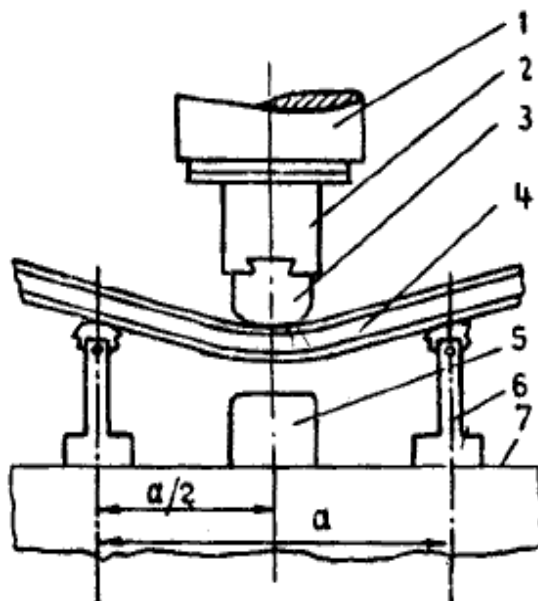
Схема правки (гибки) на прессах типа ПП-250: 1 – плунжер пресса; 2 – поворотный адаптер; 3 – пуансон; 4 – деталь; 5 – ограничитель хода; 6 – опора; 7 – нижняя плита пресса).
